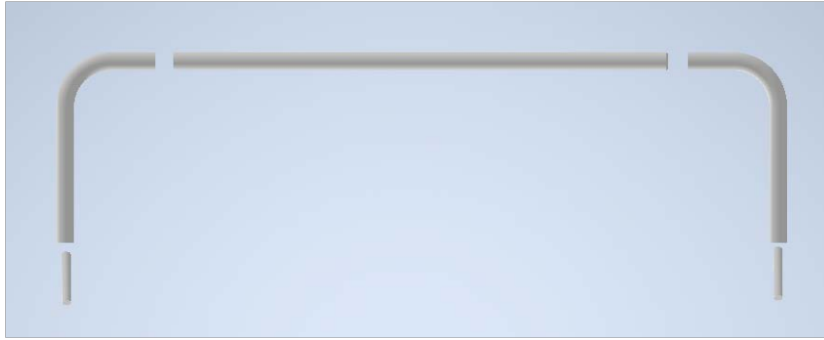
Diseño 3D y Componentes de Cable de conexión a Protoboard
